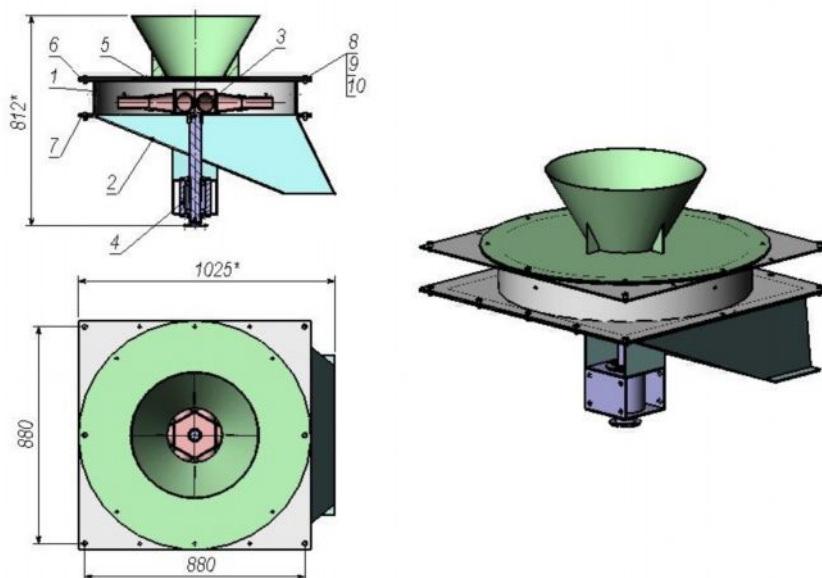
Активатор-измельчитель: 1 – цилиндрический корпус; 2 – направляющий конус; 3 – ускоритель; 4 – подшипниковый держатель вал ускорителя; 5 – приемный бункер с крышкой; 6 – верхний флянец; 7 – нижний флянец; 8 – болтовые крепления
